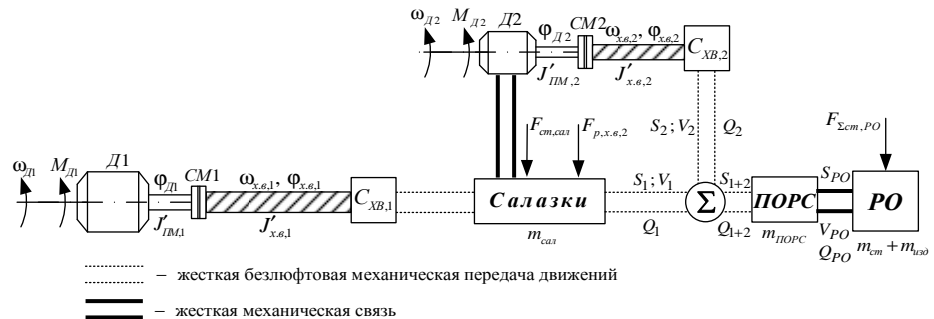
Кинематическая схема итерационного двухканального электропривода МП с двумя ВП для подачи РО металлорежущего станка
